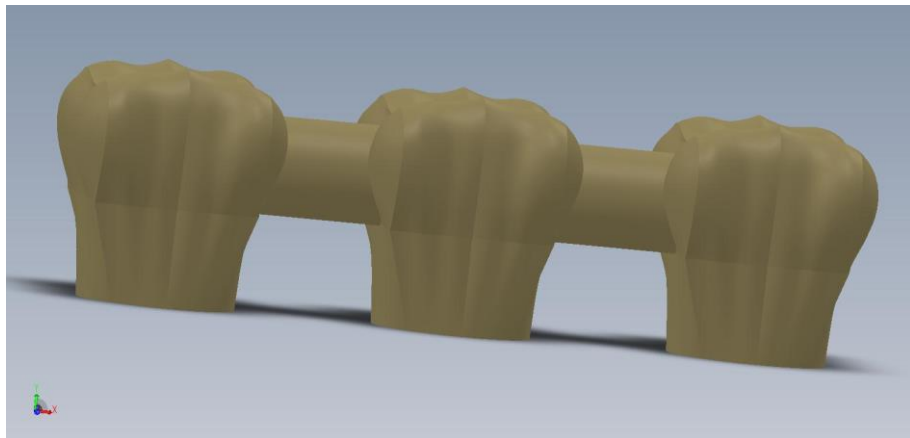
Infraestrutura metálica para suporte da cerâmica para a prótese cimentada.
